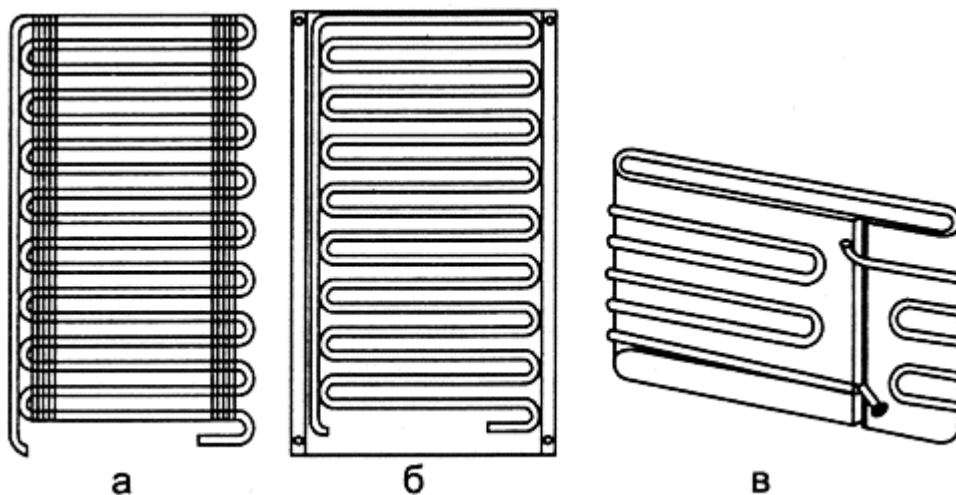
Конструкція конденсаторів холодильного агрегату:
